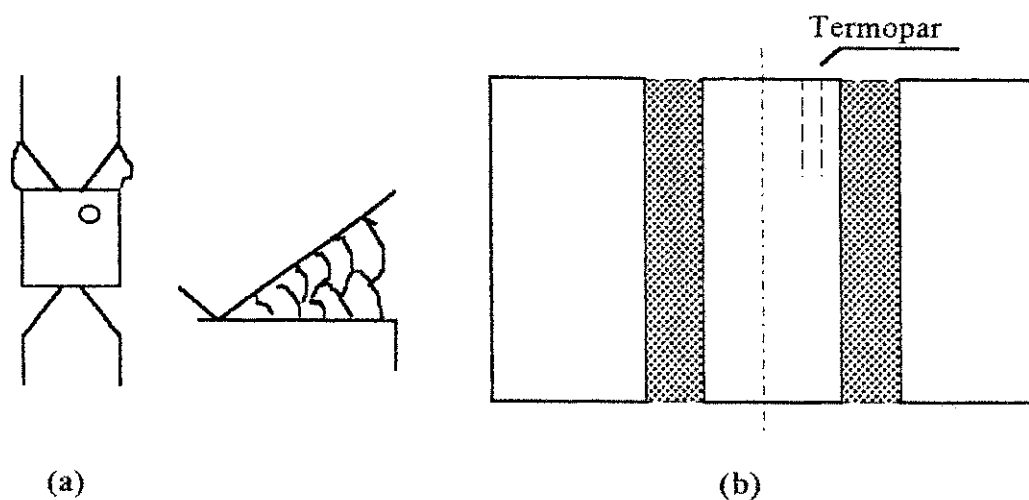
Detalhes da confecção do corpo de prova na direção "SL", Norma ASTM E 616-81[51]. (a)- Cordão de Solda (multi-passes): Eletrodo AWS E 7018, diâmetro de $2,5 \times 10^{-3} \text{ m}$ (2,5 mm); corrente de soldagem entre 80-100A. (b)- Posição do furo para a colocação do termopar para o acompanhamento da temperatura durante a soldagem do apêndice.
